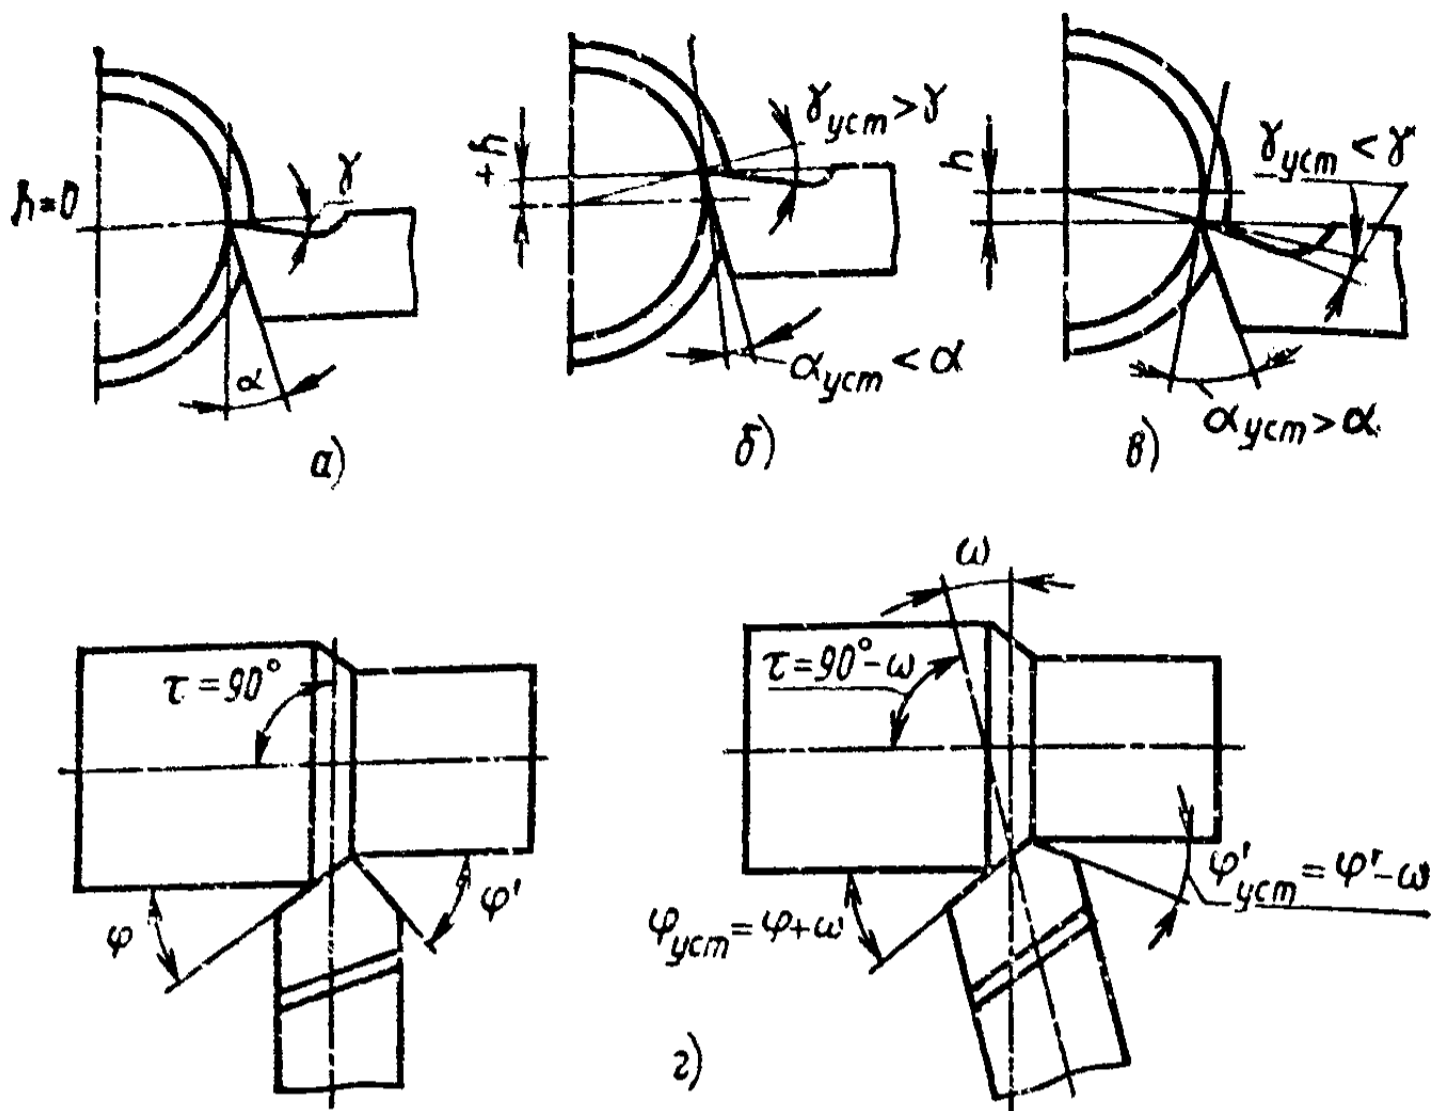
Изменение углов при установке токарного проходного резца по высоте оси заготовки (а), выше (б) и ниже (в) оси заготовки под углом  $\tau \neq 90^\circ$  (г)
